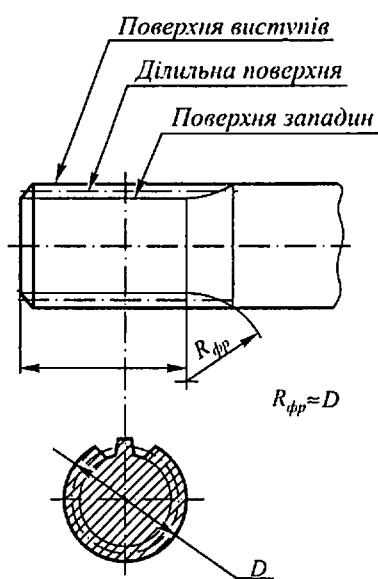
Шліцьовий вал із зубцями евольвентного профілю
